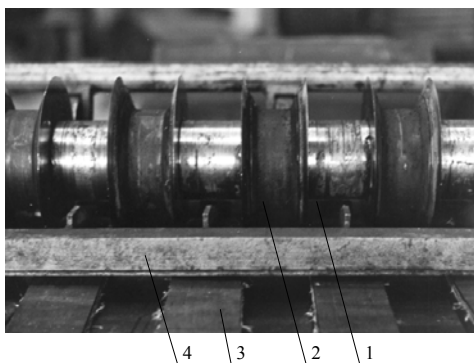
Ножовий блок установки для розрізання конвеєрної стрічки
